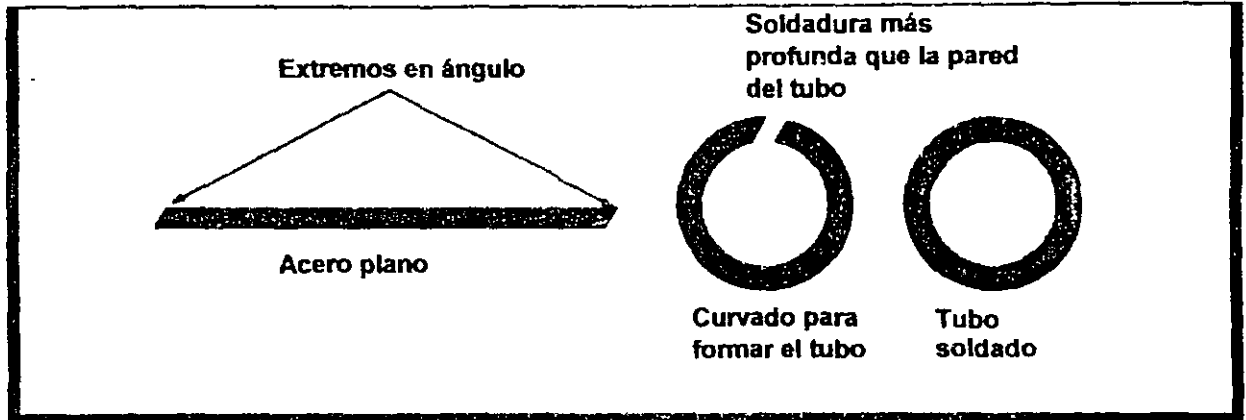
Esquema de fabricación del tubo con soldadura de solapa
